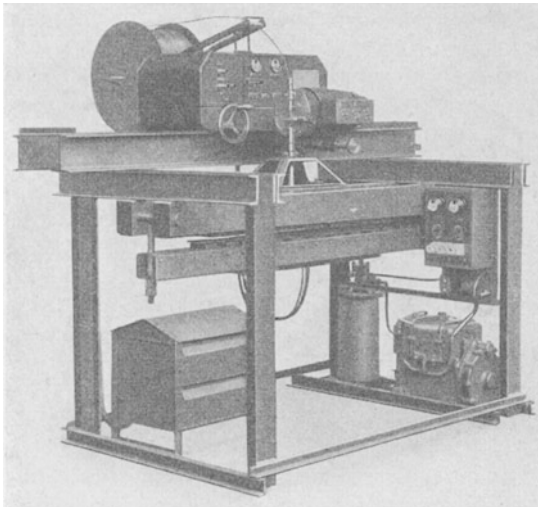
Automatische Längsnahtschweißmaschine.
